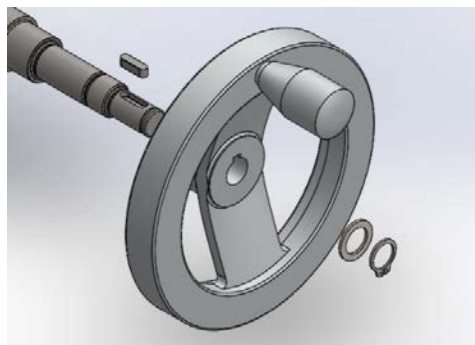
Vista explosionada de la unión entre la rueda y el husillo
